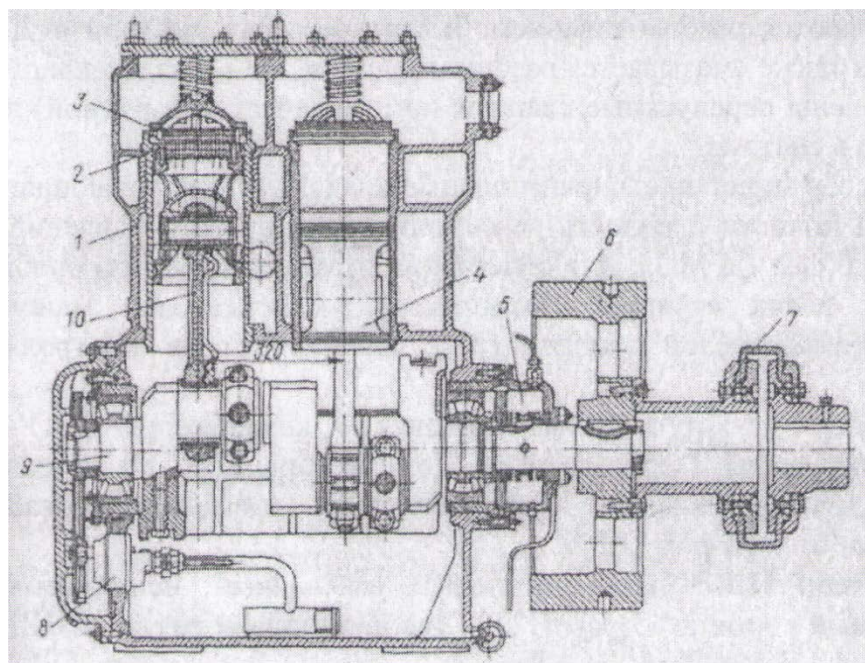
Двухступенчатый аммиачный компрессор ДАУ-80:
